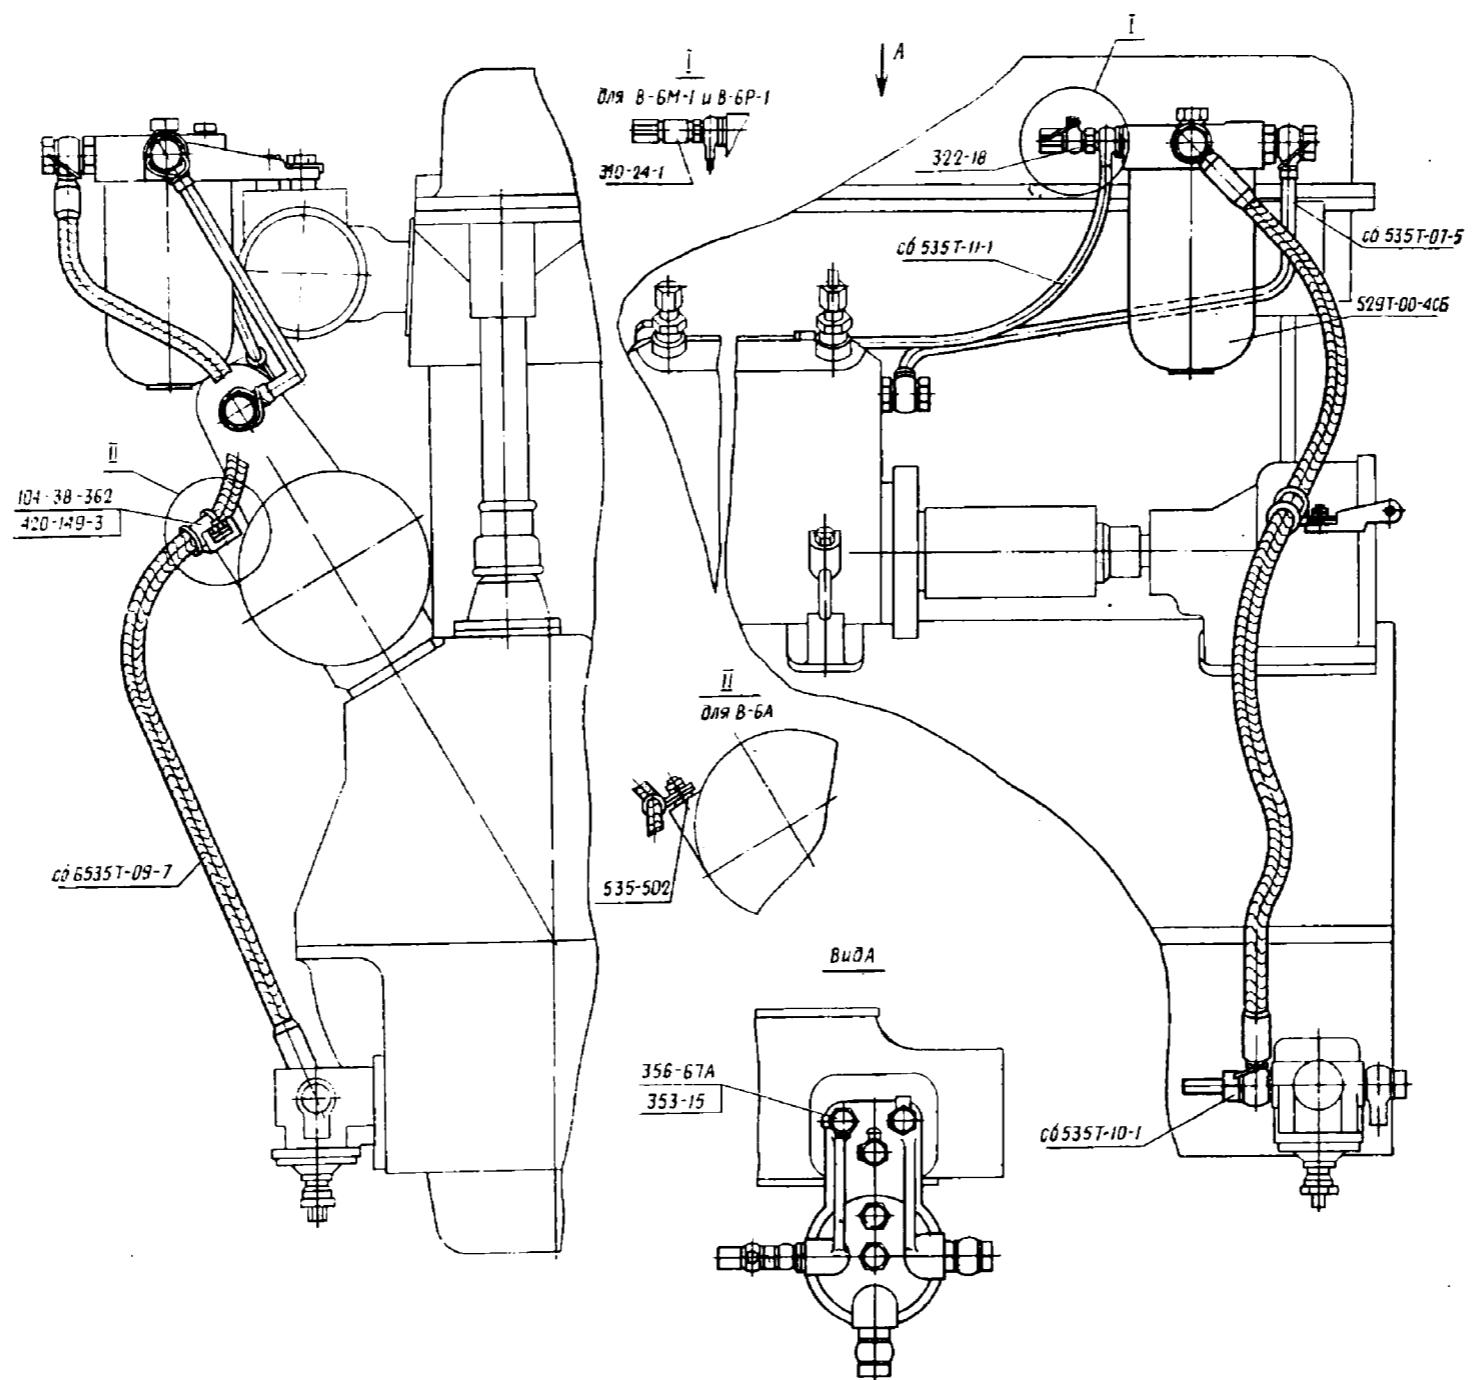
Установка топливного фильтра сб.535Т-00-5
